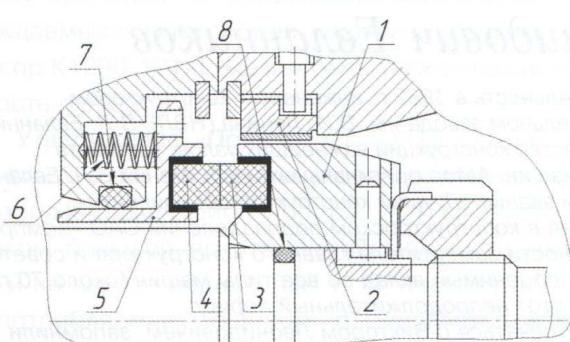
Торцовое уплотнение для центробежных компрессоров по СТП 0502-238-84:
